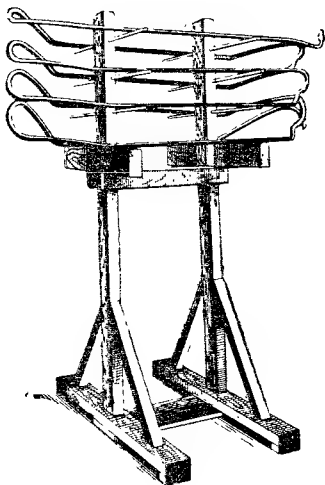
Станок-этажерка для ручной изолировки витков секций.
